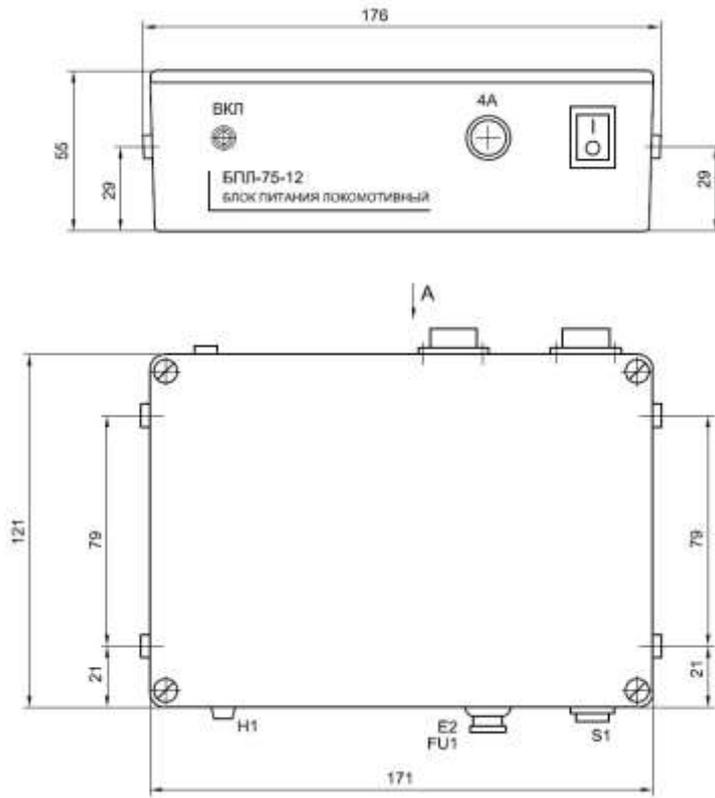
Габаритные размеры БПЛ-75-12
